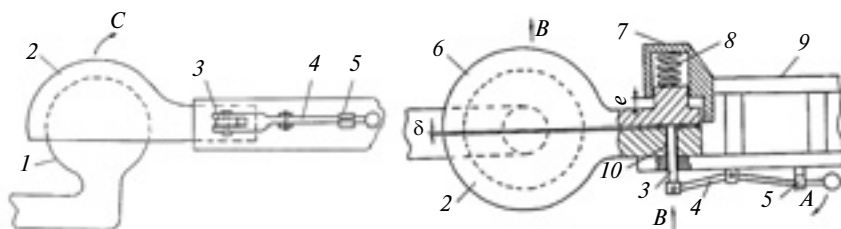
Схема тягово-цепного устройства по пат. № 2493996 РФ:
